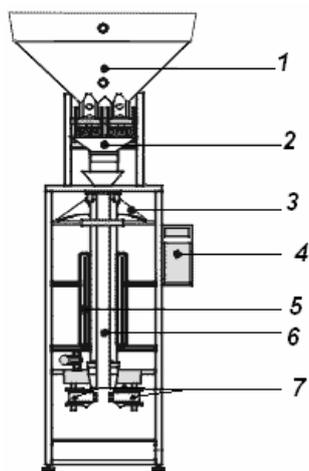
Схема вертикального фасовочно-упаковочного автомата:
